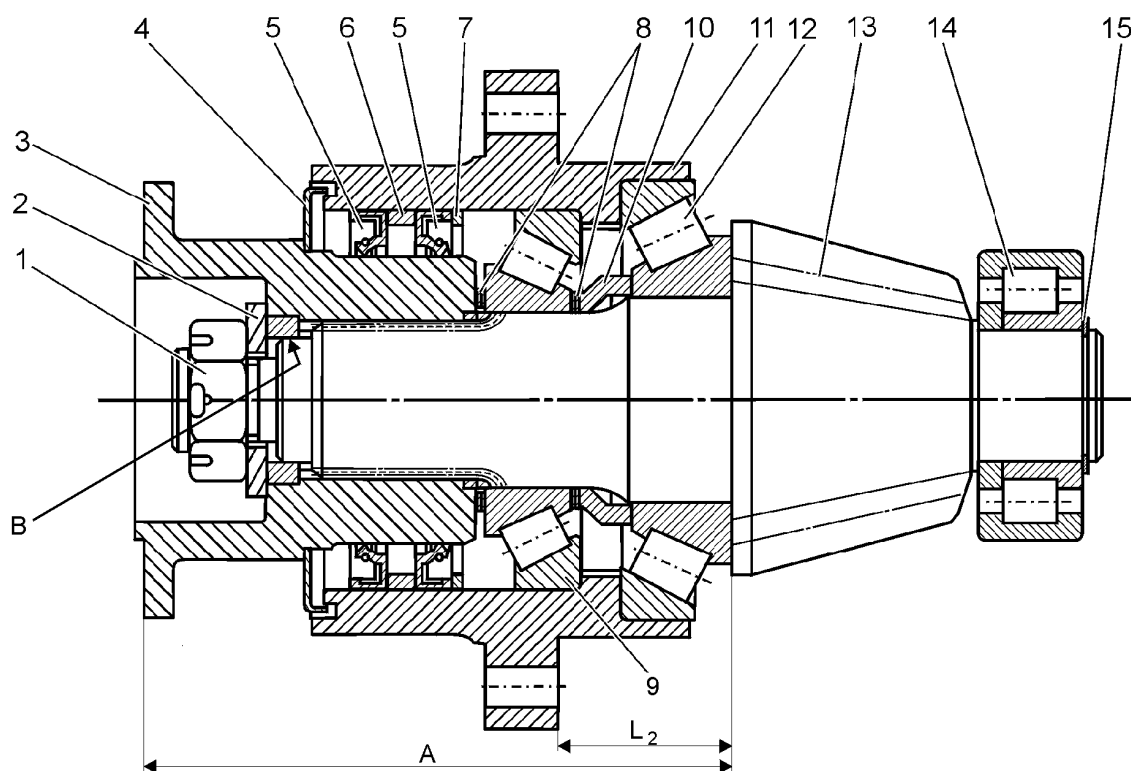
D.12. Узел вала ведущей шестерни (разрез)
